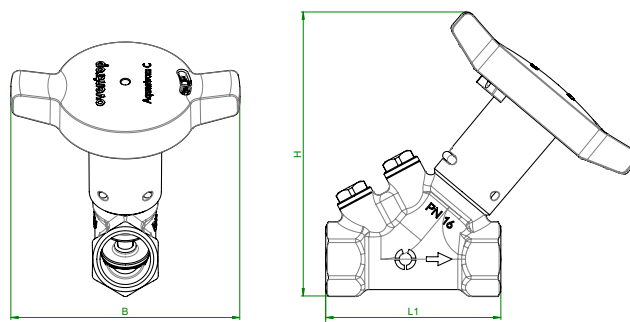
Abmessungen Seitenansicht / Frontansicht Innengewinde ohne Zubehör
